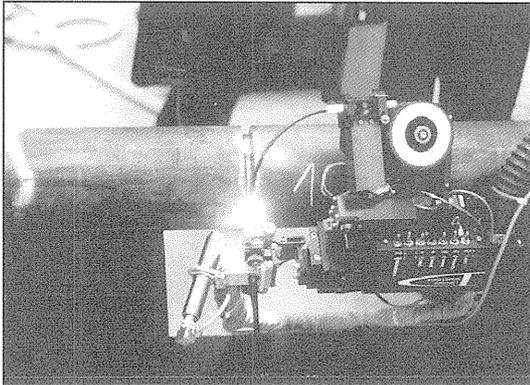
Temperaturmessung während des Schweißens zur Steuerung der Kühlung. Die Kälte des Formiergases wird zur Kühlung der Schweißnaht genutzt.
